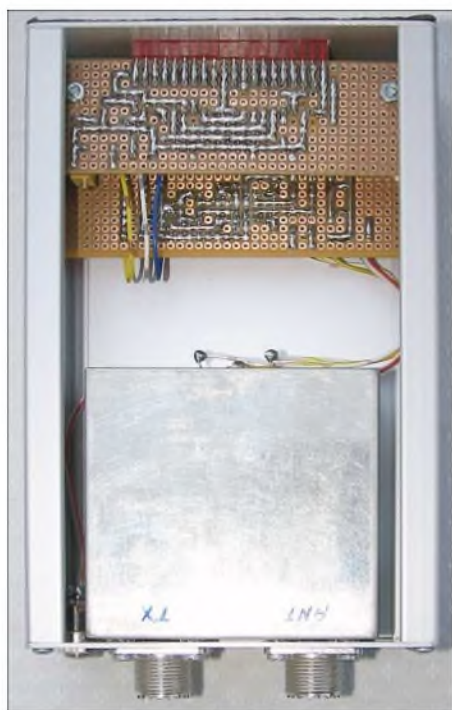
Das geöffnete Gehäuse lässt die Anordnung der Baugruppen im Euro-Gehäuse erkennen. Die Verdrahtung der Baugruppen untereinander beschränkt sich auf wenige Drähte. Fotos: DL4FBM, Hanisch
